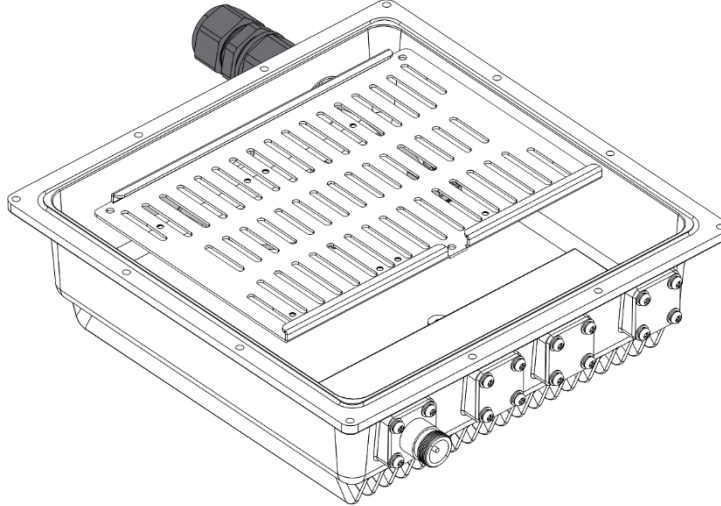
□ Montageplatte im Gehäuse der RAKBox-GW-3
